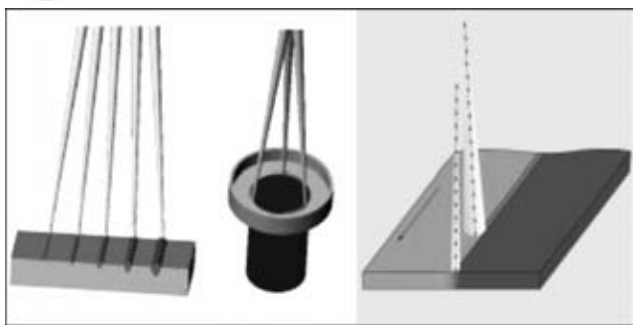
Электронно-лучевая сварка с параллельными швами
